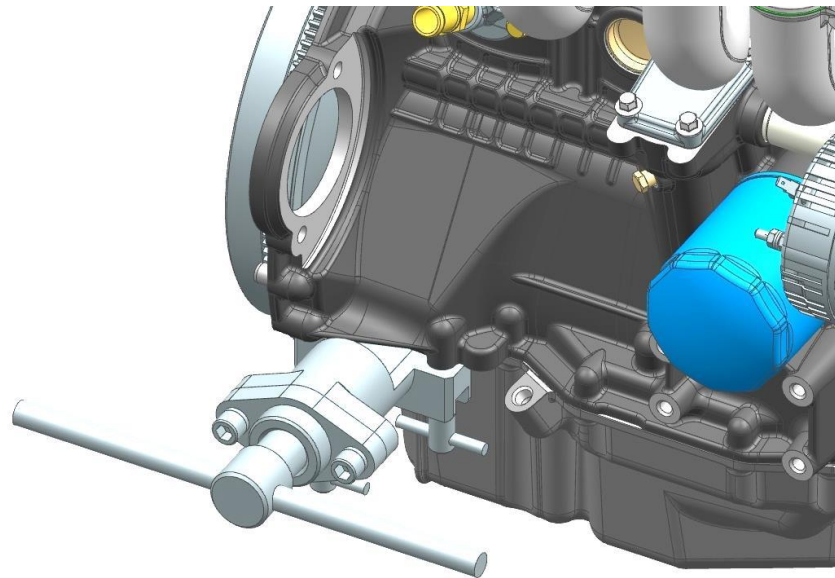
Установка приспособления ЗМ 7823-4815 на двигателе
